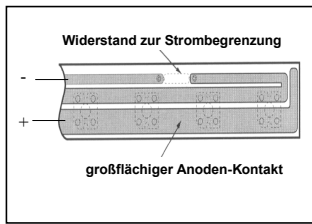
Visualisierung der Design-Rules (PCB-Rückseitenansicht)
